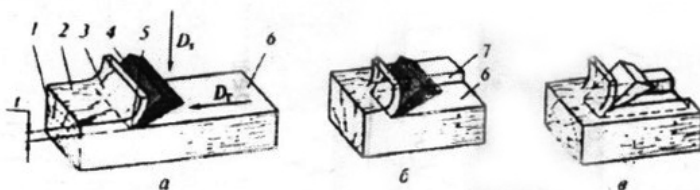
Схемы резания: а – открытое; б – полузакрытое; в – закрытое; 1 – заготовка; 2 – обрабатываемая поверхность; 3 – стружка; 4 – резец; 5 – режущая кромка; 6 – поверхность резания; 7 – боковая поверхность резания
